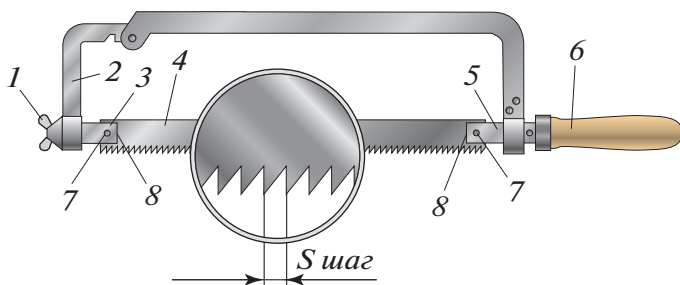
Ручная слесарная ножовка с раздвижной рамкой
